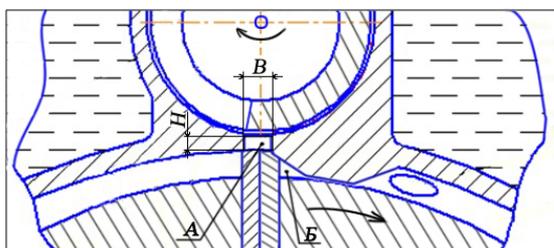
Камера сгорания роторного двигателя РДТ-1
